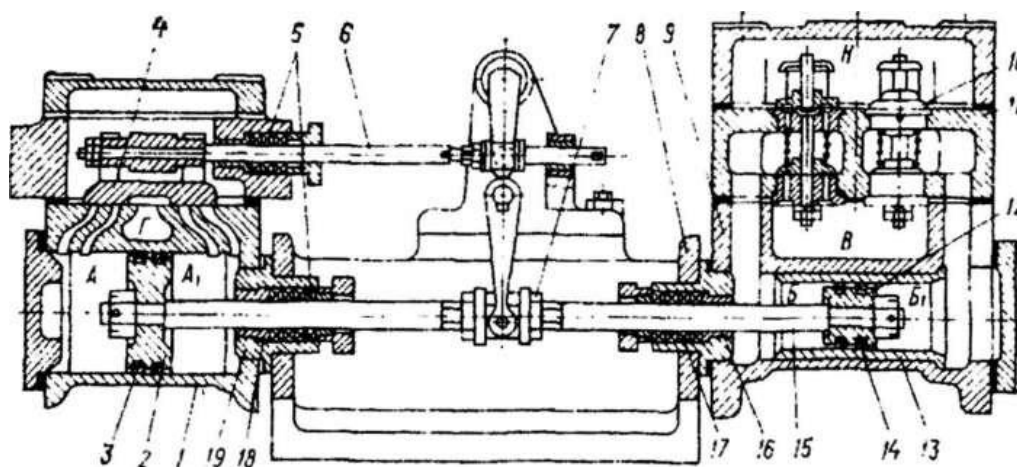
Поршневой паровой насос типа ПДГ: 1 - блок паровых цилиндров; 2 - паровой поршень; 3, 14 – уплотнительные кольца; 4 - золотник; 5, 17 - сальниковая набивка; 6 - шток золотника; 7 - муфта; 8 - средник; 9 - блок гидравлических цилиндров; 10 - тарельчатый клапан; 11 - клапанная камера; 12 - гидравлический поршень; 13 - втулка; 15 - шток; 16, 18 - грундбуксы; 19 - корпус сальника; А, А<sub>1</sub>, Б, Б<sub>1</sub>, В, Г, Н – камеры
